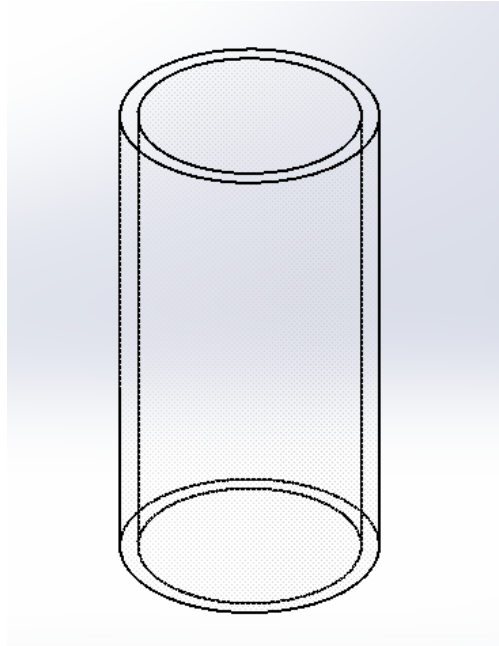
Верхня циліндрична камера – матеріал «Glass»
